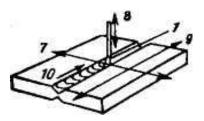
Классификация магнитных полей по отношению к сварочной дуге (1-7 - поперечное; 8 - продольное; 9 - параллельное; 10 - по направлению сварки)
